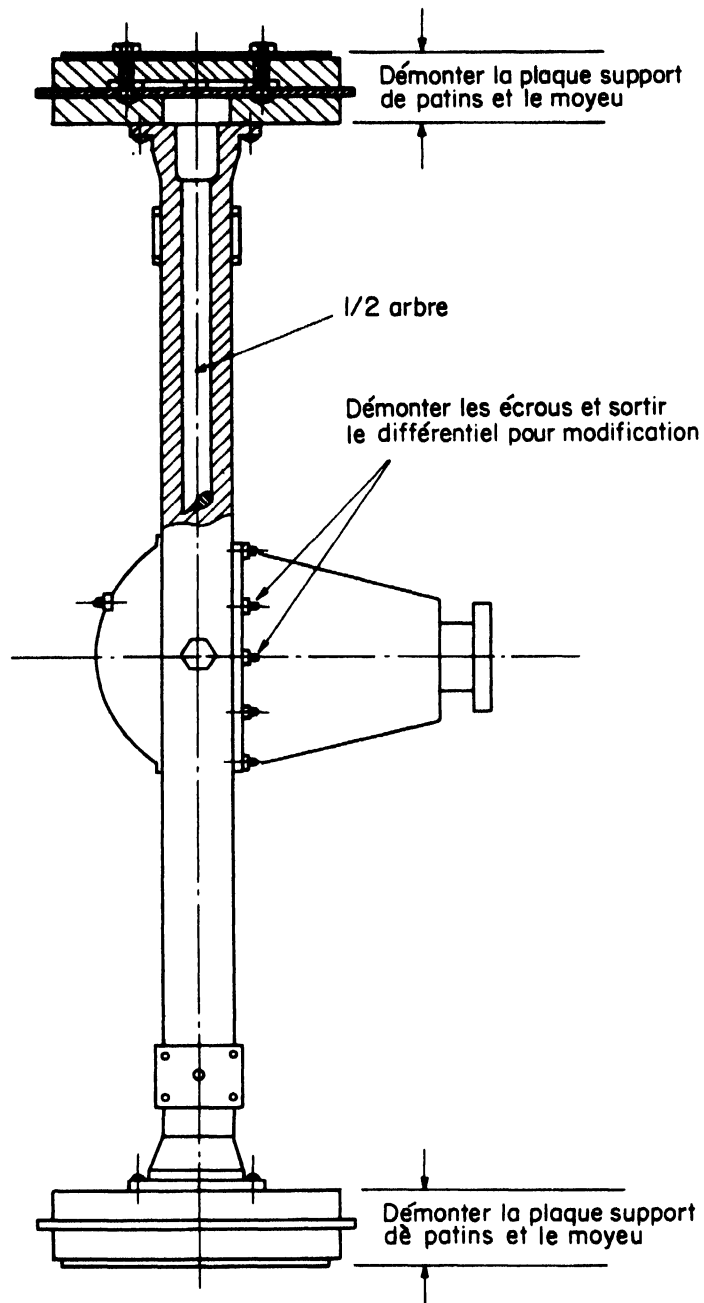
DEMONTAGE DU PONT-ARRIERE
